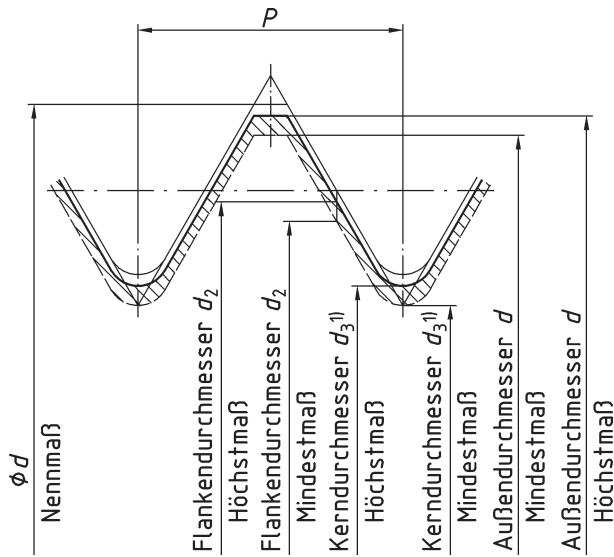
Außengewinde mit Toleranzfeldlagen e, f, g
